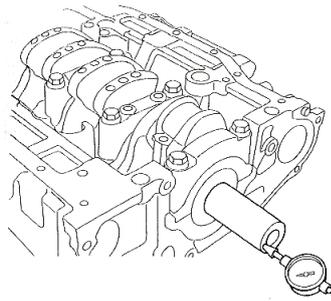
Medición del juego axial del cojinete principal del cigüeñal.
